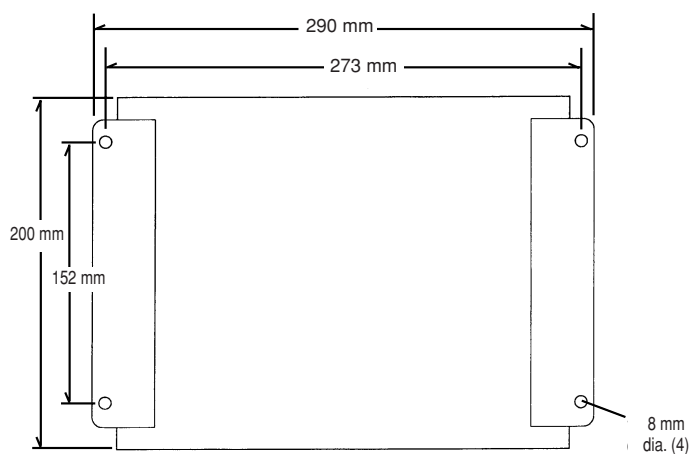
Dimensioni di montaggio – consolle remota ad alta frequenza
